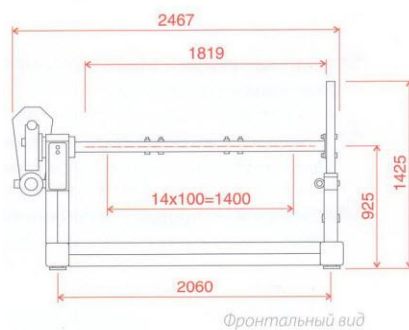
Стенд Р-776Е (габаритные размеры)
